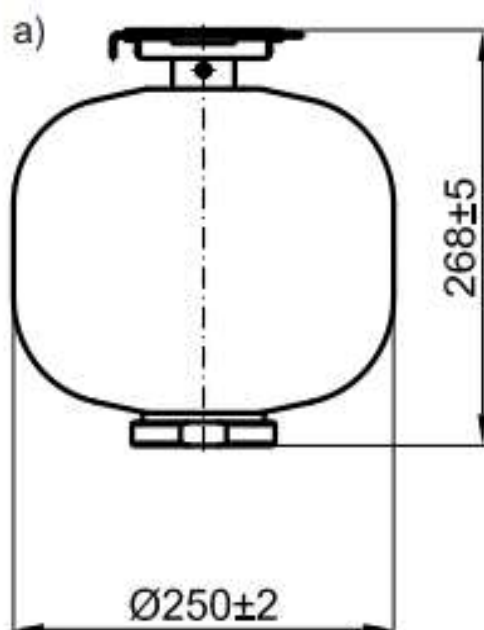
Общий вид и габаритные размеры модуля порошкового пожаротушения потолочного крепления Буран-8У
